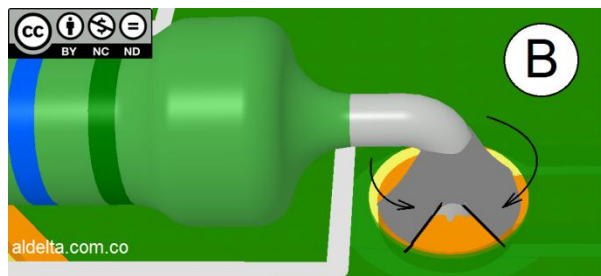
Mojado circunferencial de componente THT en la cara TOP, arriba o lado destino de la soldadura según la IPC 610. Autoría propia.
